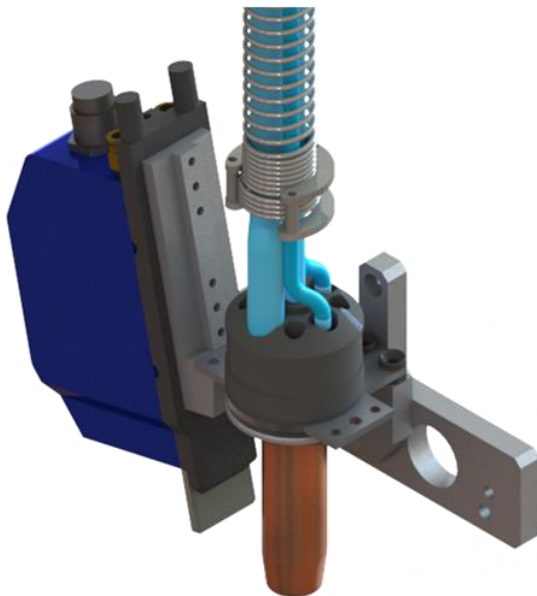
Representação em CAD da montagem do conjunto Tocha/Laser.
